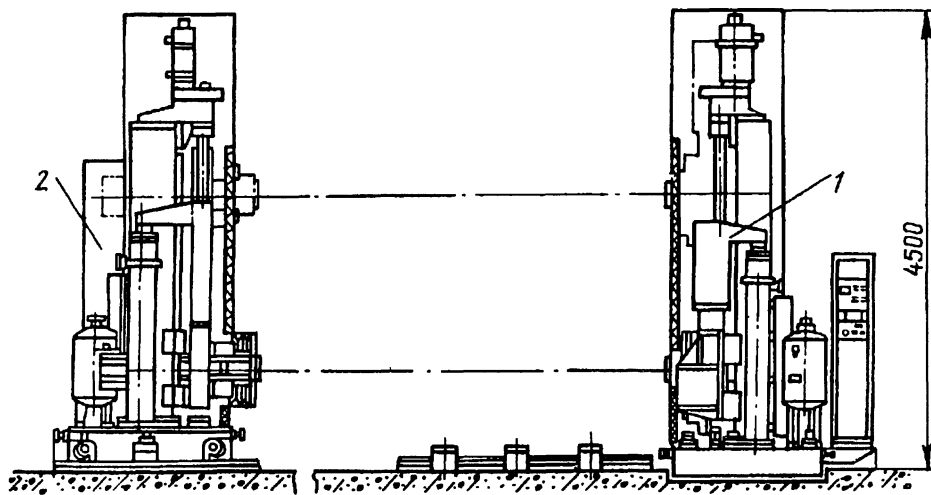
Сварочный горизонтальный вращатель с программным управлением М150730:
